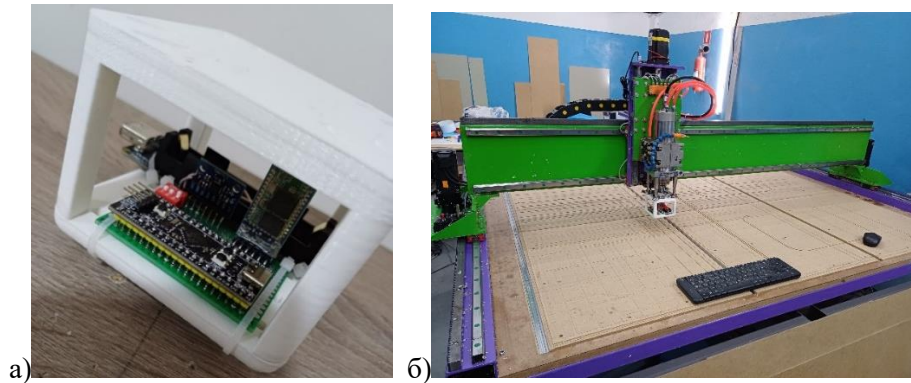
Зображення роздрукованого корпусу а) та випробувального стенду б) на базі CNC станка з прикріпленням інерційним модулем.
